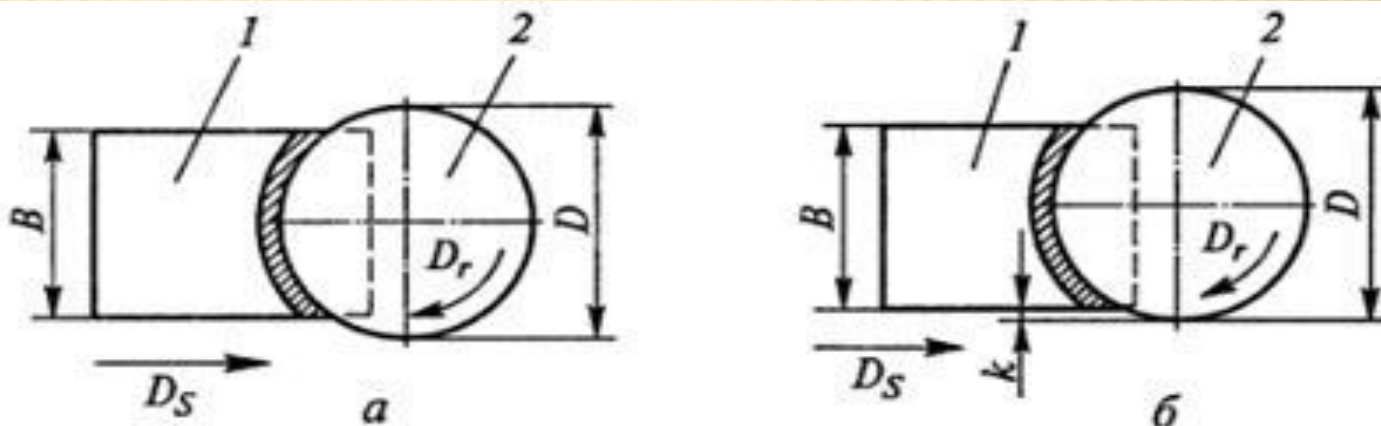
Установка торцовой фрезы относительно заготовки:
